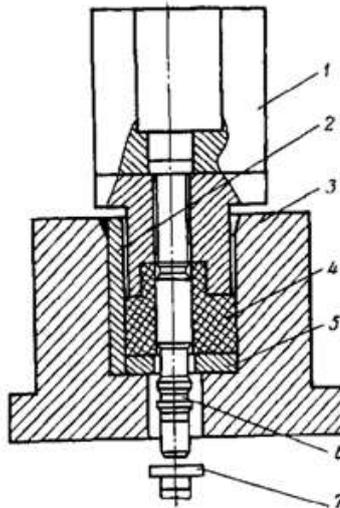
Схема приспособления для обжатия втулок:
